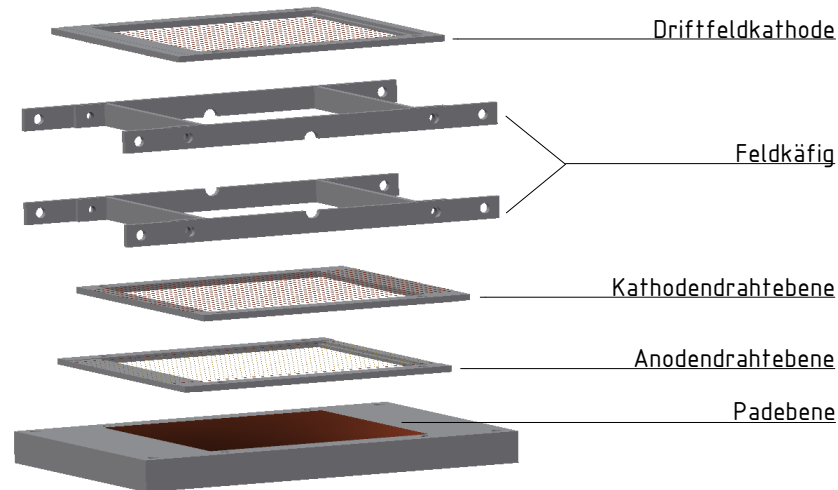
Explosionszeichnung der verwendeten Drahtkammer im Laboraufbau am IKF. Die Quellenhalterung befindet sich in dieser Ansicht oberhalb der Driftkathode. [Sch14]
